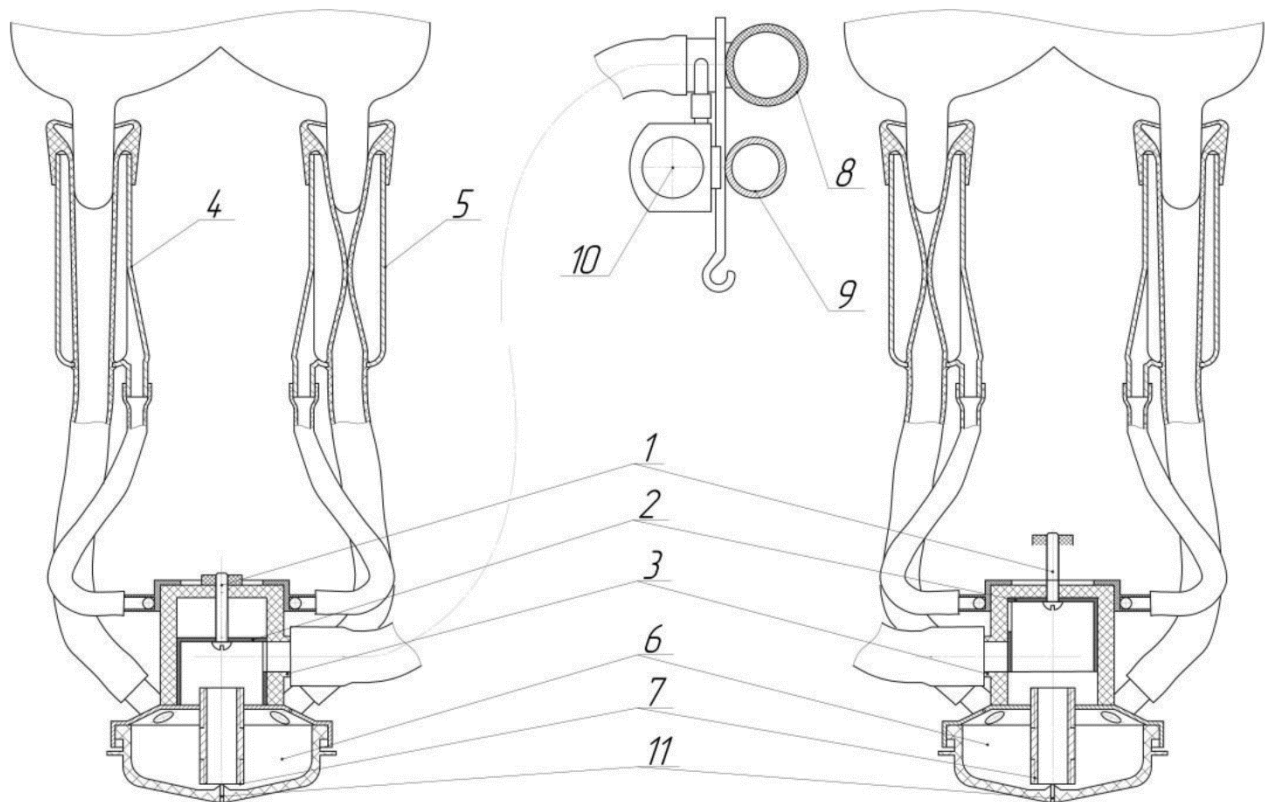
Схема експериментального зразка доїльного апарата: 1 – гвинт; 2 – клапан; 3 – корпус колектора; 4 – вакуумний патрубков; 5 – стакан; 6 – молокозбірна камера колектора; 7 – відвідна трубка; 8 – молокопровід; 9 – вакуумпровід; 10 – кран; 11 – отвір подачі повітря в колектор
